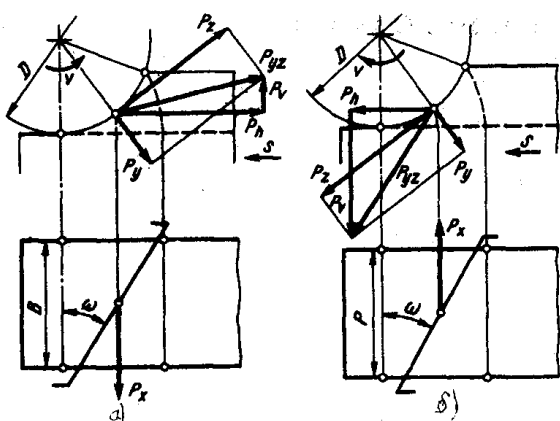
Составляющие силы резания при фрезеровании цилиндрической фрезой: а - при встречном фрезеровании (против подачи); б — попутном (в направлении подачи)
